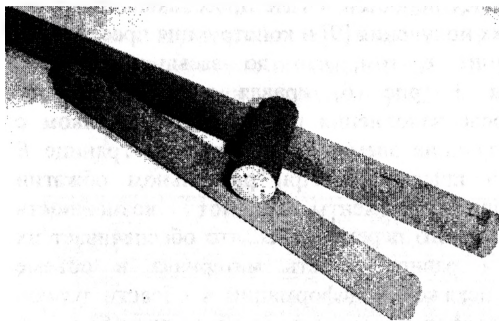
Вид заготовок из твердого сплава с двумя сквозными отверстиями
